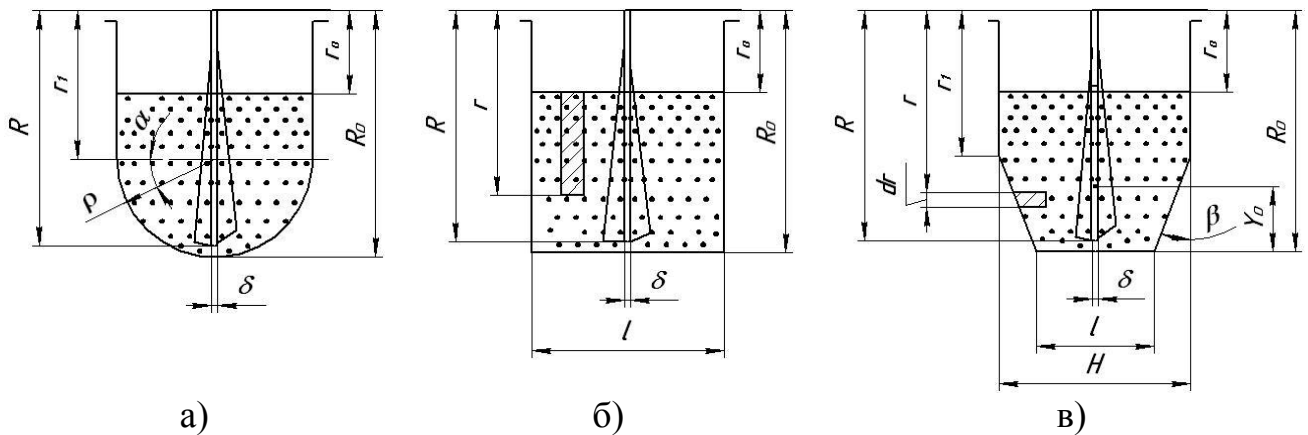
Геометрические параметры механизмов блокировки с торовой (а), цилиндрической (б) и конической (в) формой внутренней полости
